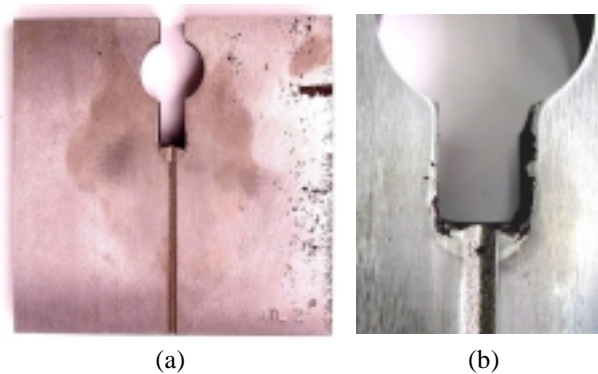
(a) Probeta CCA. (b) Detalle de soldadura.
